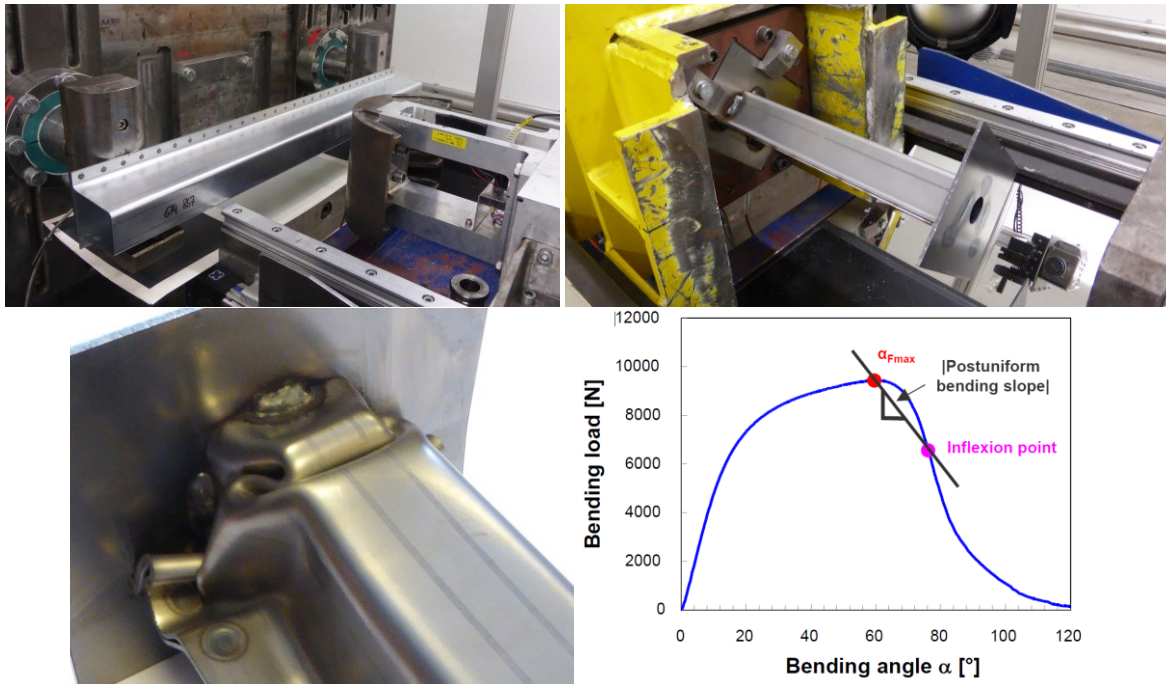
Versuchsaufbau für Seitencrashtest (links oben) und Axialcrashtest (rechts oben). Verformung des axialen Crashträgers beim Aufprall der Crashmasse (links unten); Definition des Post-Uniform Bending Slope (PUBS) nach [3] (rechts unten).
